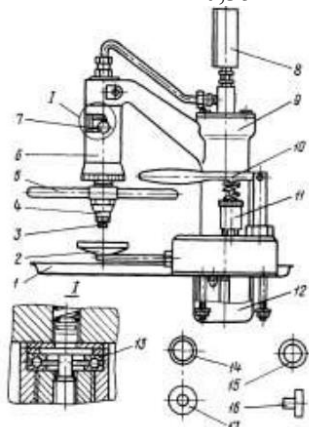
Прилад для випробовування нагнітальних клапанів: 1 – піддон; 2 - лоток зливний; 3 – тріщотка; 4 - головка мікрогвинта; 5 – вороток; 6 - механізм затиску; 7 – ручка; 8 – манометр; 9 – корпус; 10 - ручка насоса; 11 – ручний насос; 12 – бачок; 13 – підшипник; 14,15 – кільця; 16 – заглушка; 17 – прокладка.
